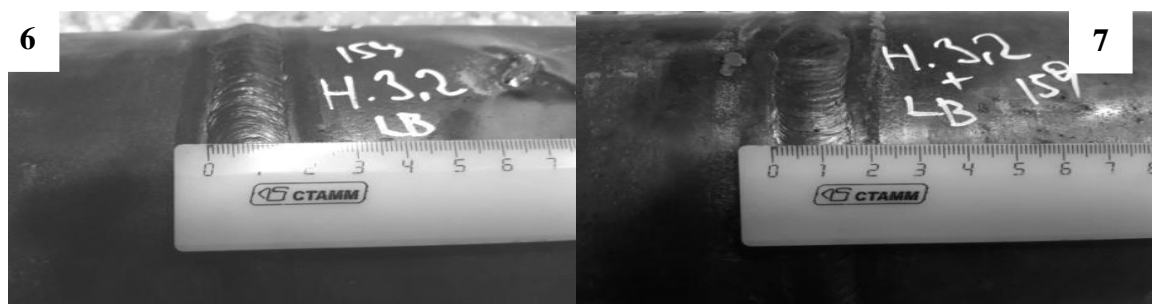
Сварное соединение 6. Рисунок Б27. Сварное соединение 7.
